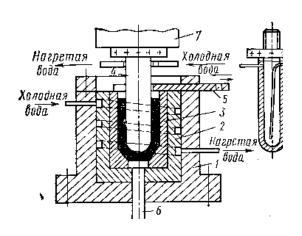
Схема штампа для обратного выдавливания поковки снаряда на гидравлическом прессе:
